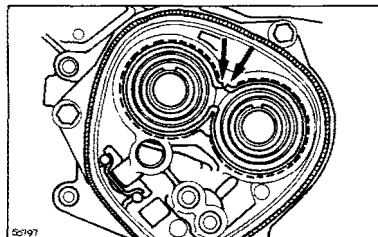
Положение фиксирующих колец в картере коробки передач
